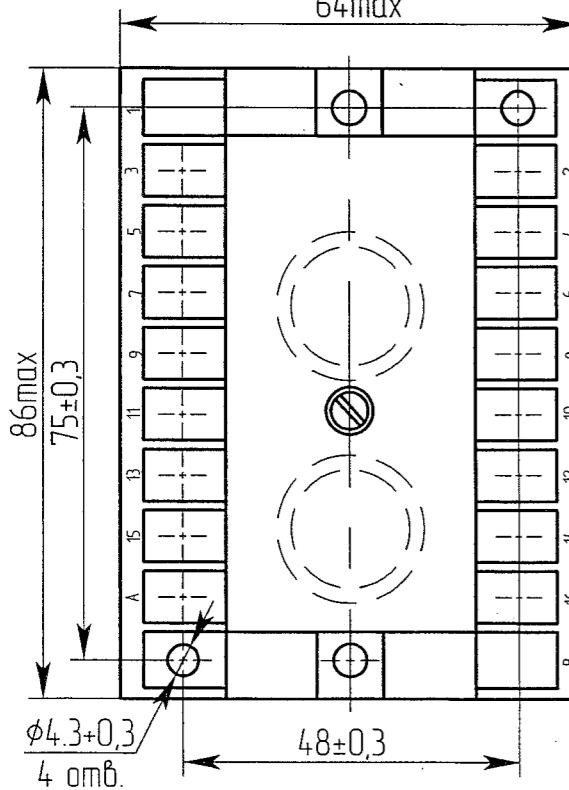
Реле типов PCB18-13-XXXX1, PCB18-23-XXXX1,
